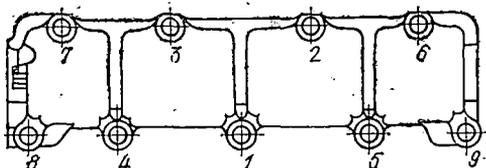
Порядок затяжки гаек крепления корпуса подшипников распределительного вала
